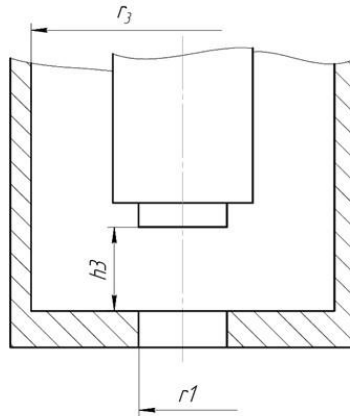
Розрахункова схема дозувально-фасувального пристрою із каналом циліндричної форми
